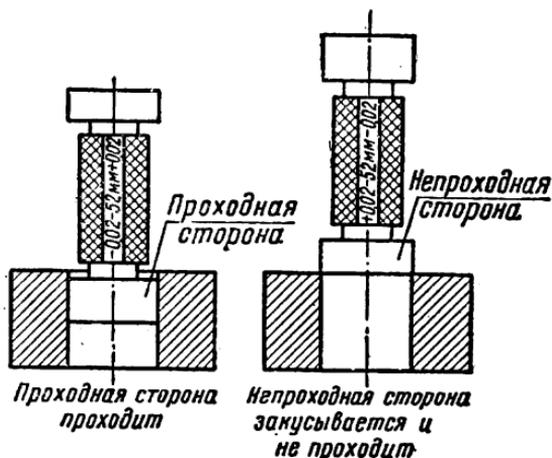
Предельный калибр-пробка для проверки размеров отверстия.
